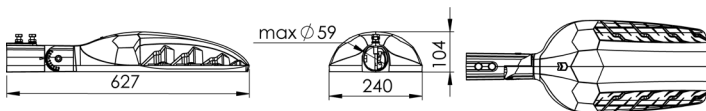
Общий вид светильника Street X1 Pro с консольным поворотным креплением.
